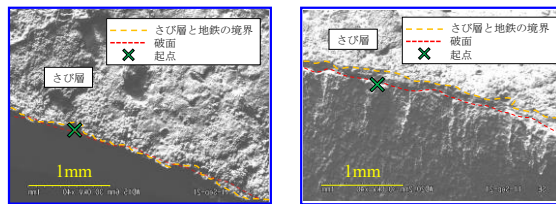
SEM での観察結果(十字すみ肉溶接継手 3 体目)
